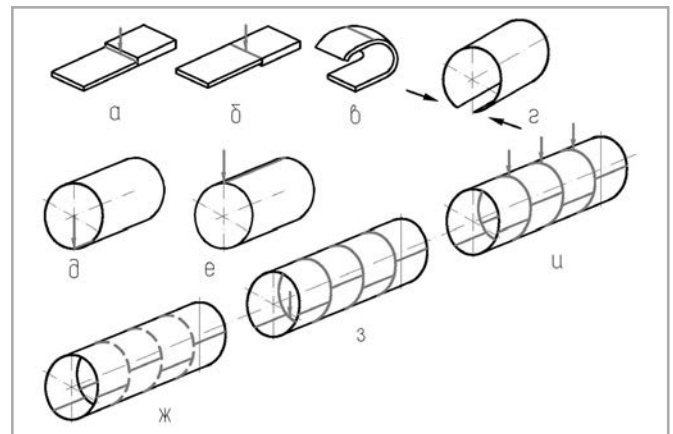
Схема технологического процесса изготовления обечайки из 4-х царг: а — сборка и автоматическая сварка первой стороны развертки царги из 2-х частей; б — автоматическая сварка второй стороны развертки царги; в — вальцовка царги; г — сборка замыкающего стыка царги; д — автоматическая сварка внутреннего шва замыкающего стыка царги; е — автоматическая сварка наружного шва замыкающего стыка царги; ж — сборка обечайки из 4-х царг; з — сварка внутренних кольцевых швов обечайки; и — сварка наружных кольцевых швов обечайки
